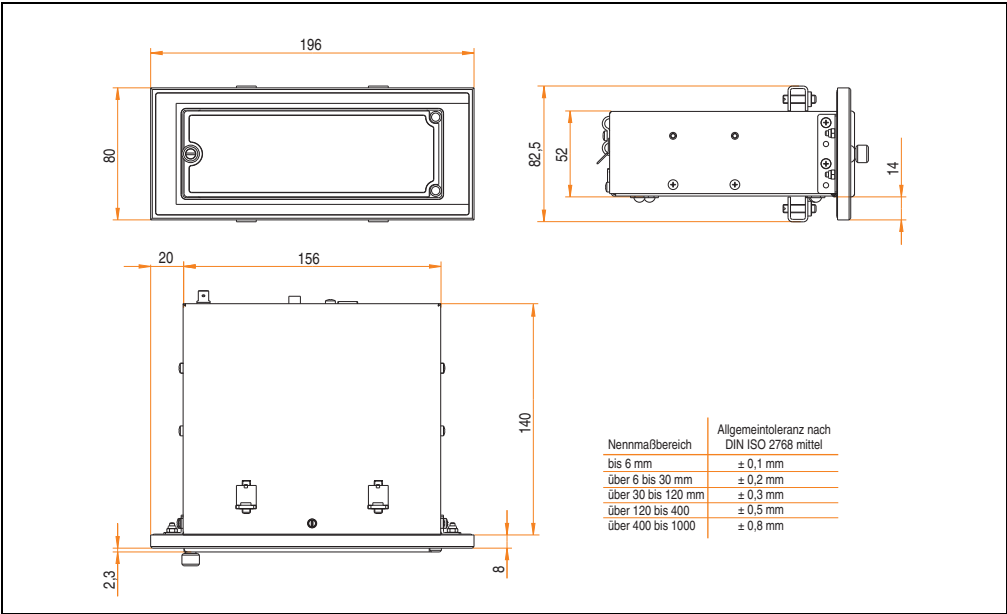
Abmessungen USB Media Drive mit Frontklappe
